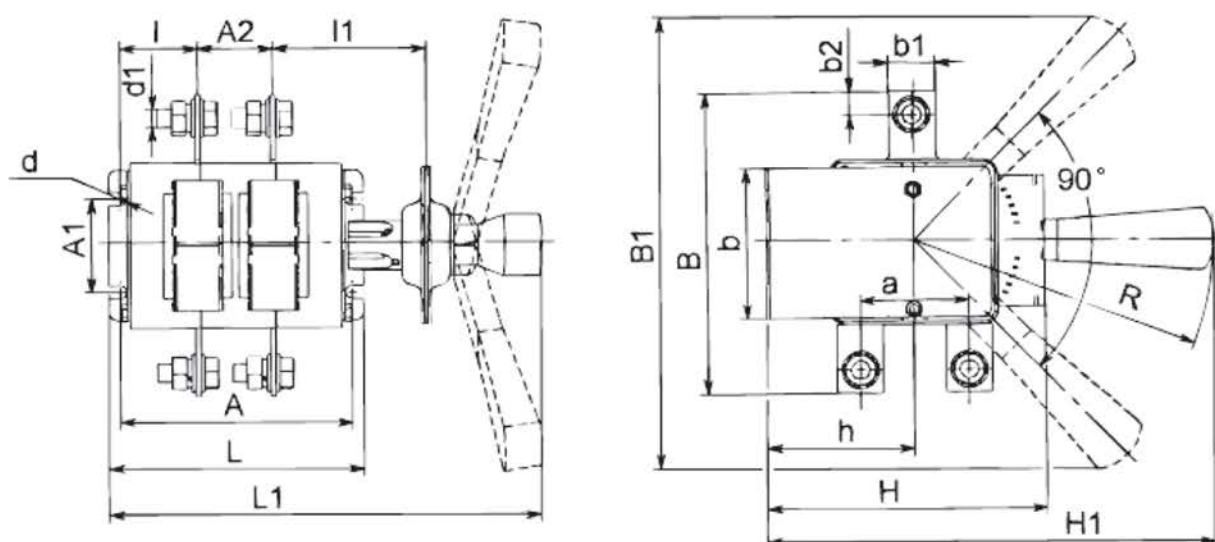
Выключатель-разъединитель двухполюсный на два направления с передней смещенной рукояткой.
